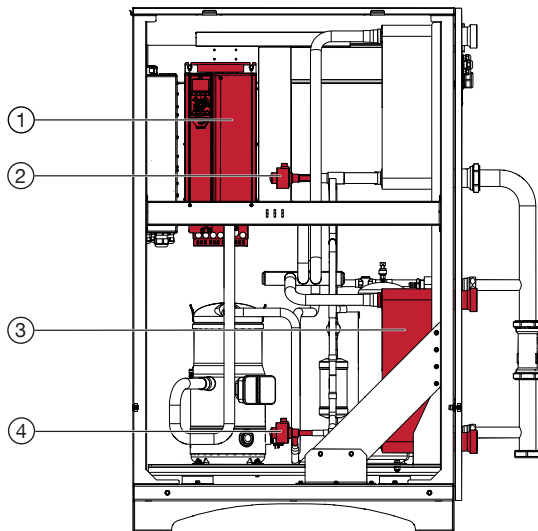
Wärmepumpe geöffnet – Ansicht von rechts
